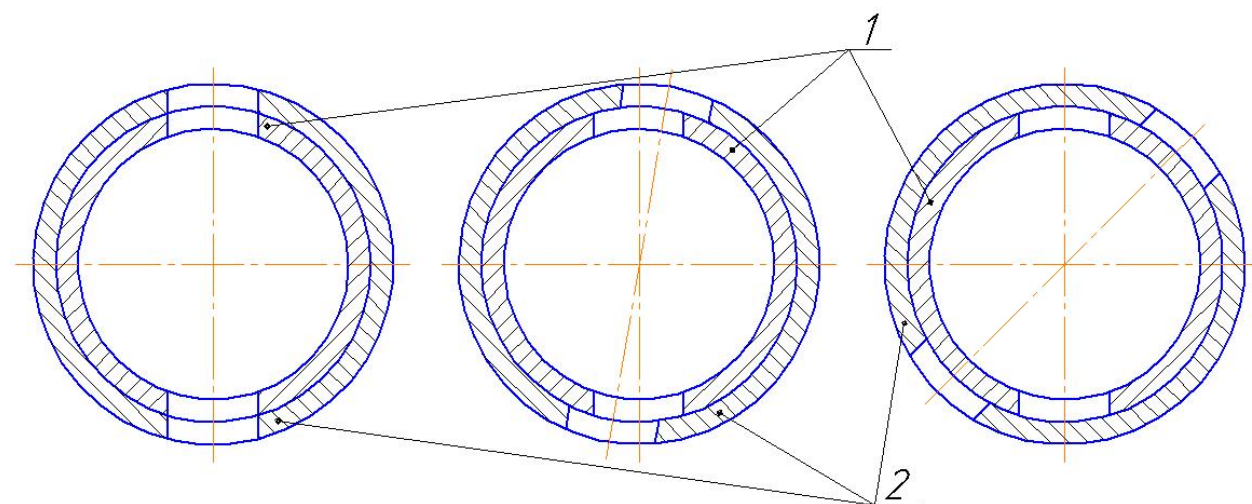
Схема устройства для выхода газов с помощью поворотного кольца на корпусе и её различные положения во время работы
